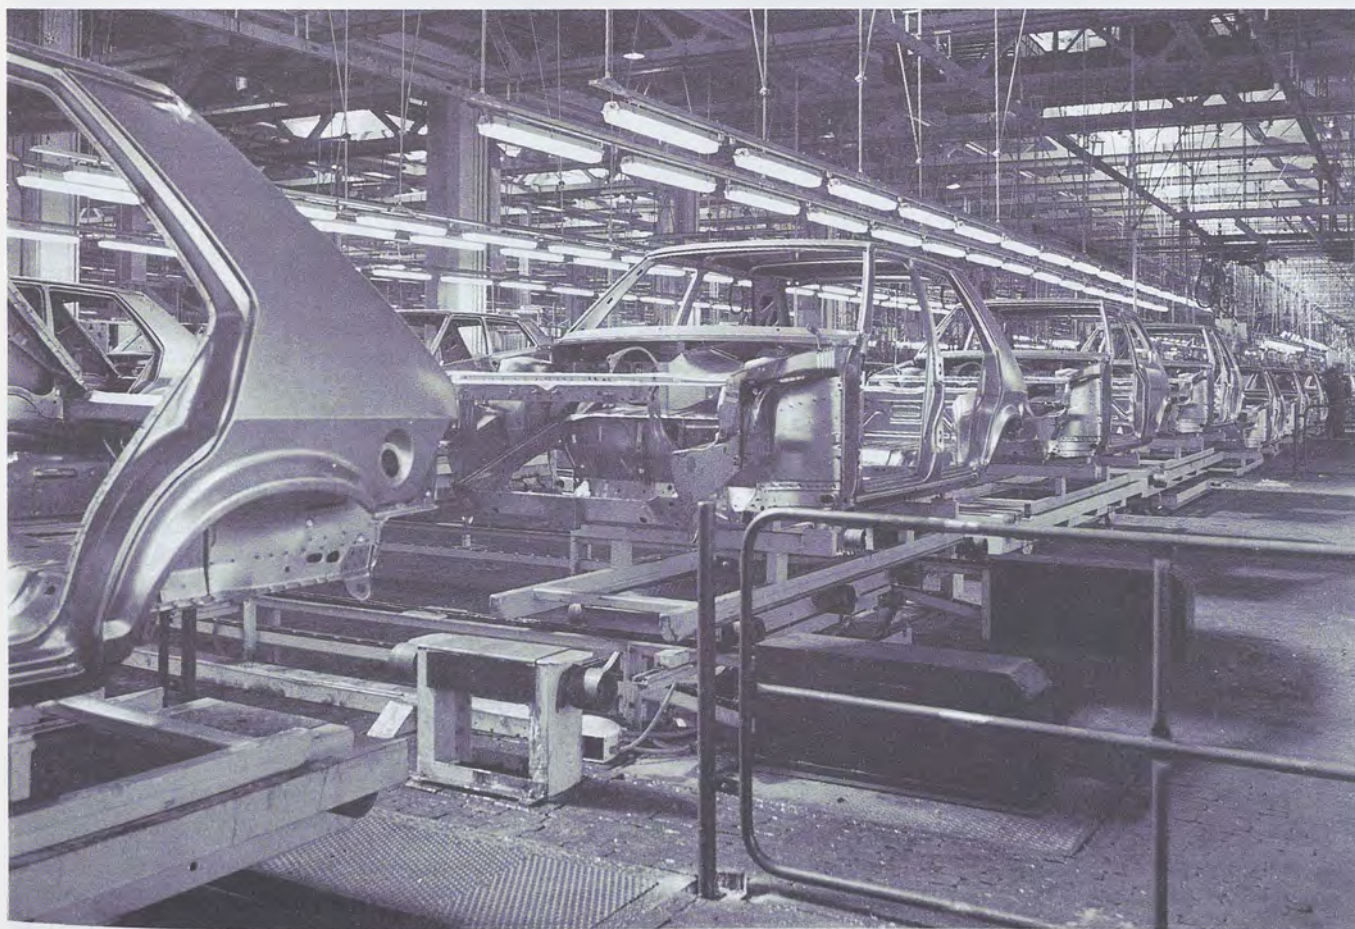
Trasportatori a skid per scocche di autovetture.
